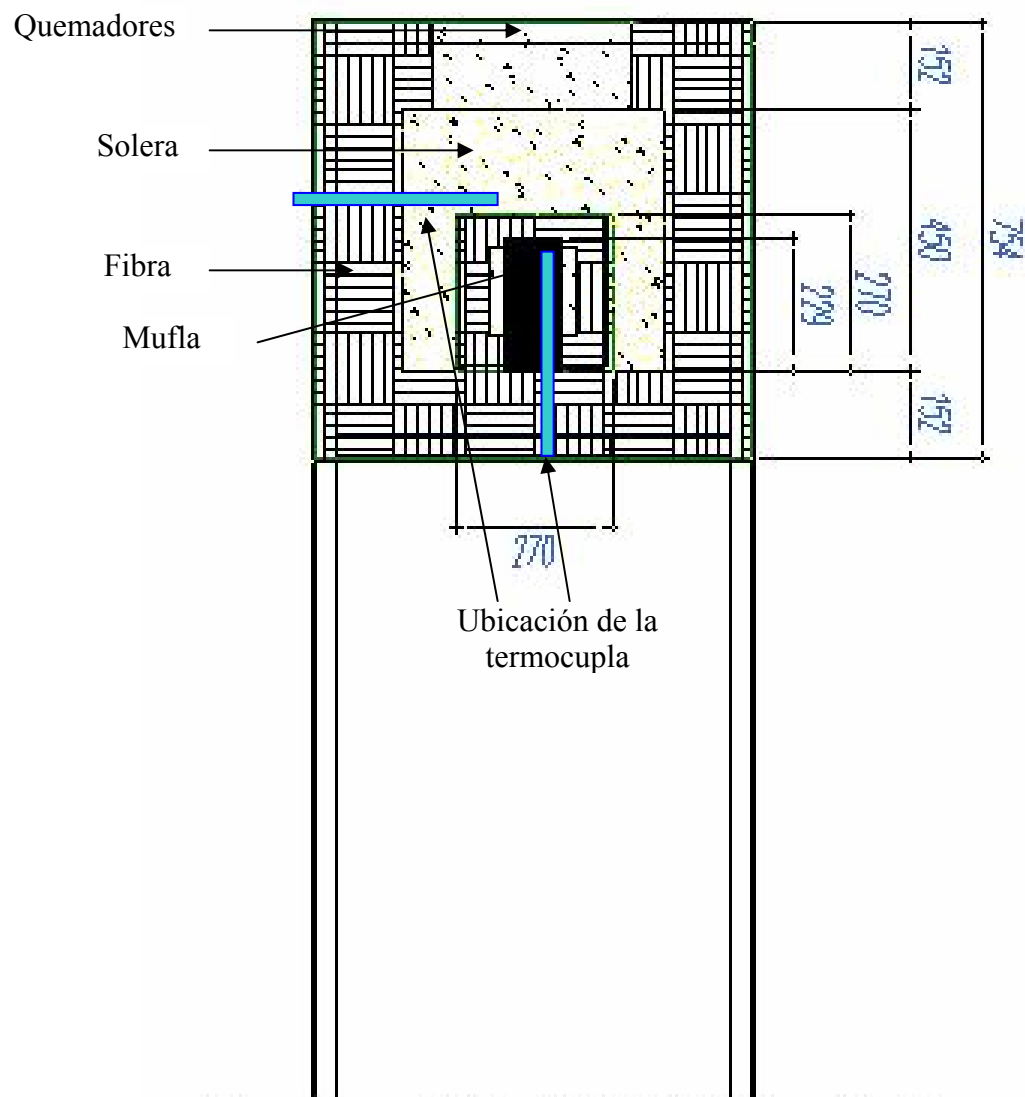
Vista Frontal Sin Incluir La Chimenea
